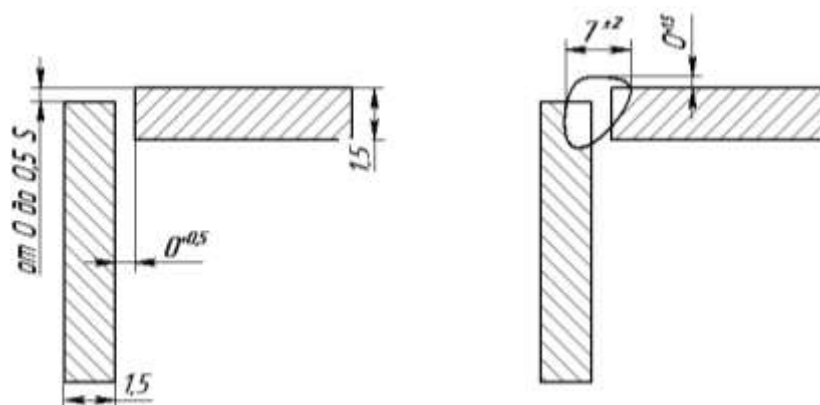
Конструктивные элементы сварного соединения У4
